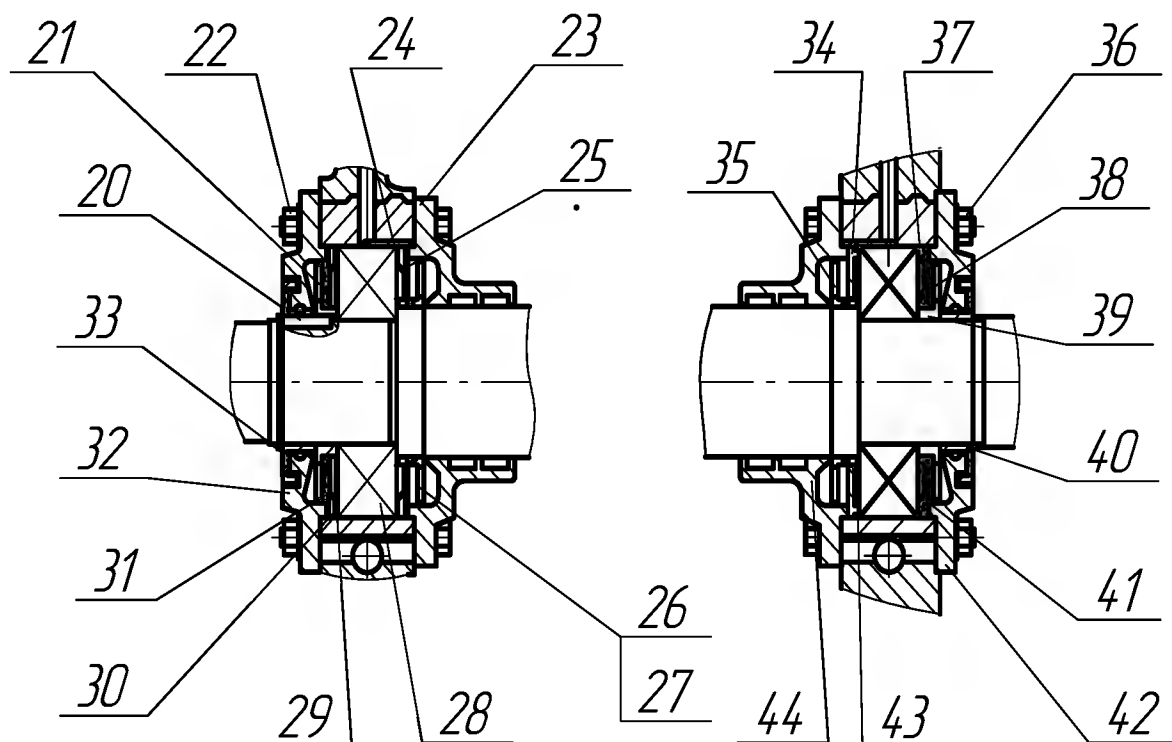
Подшипниковые щиты двигателя рДМ180М2 IM 3912
